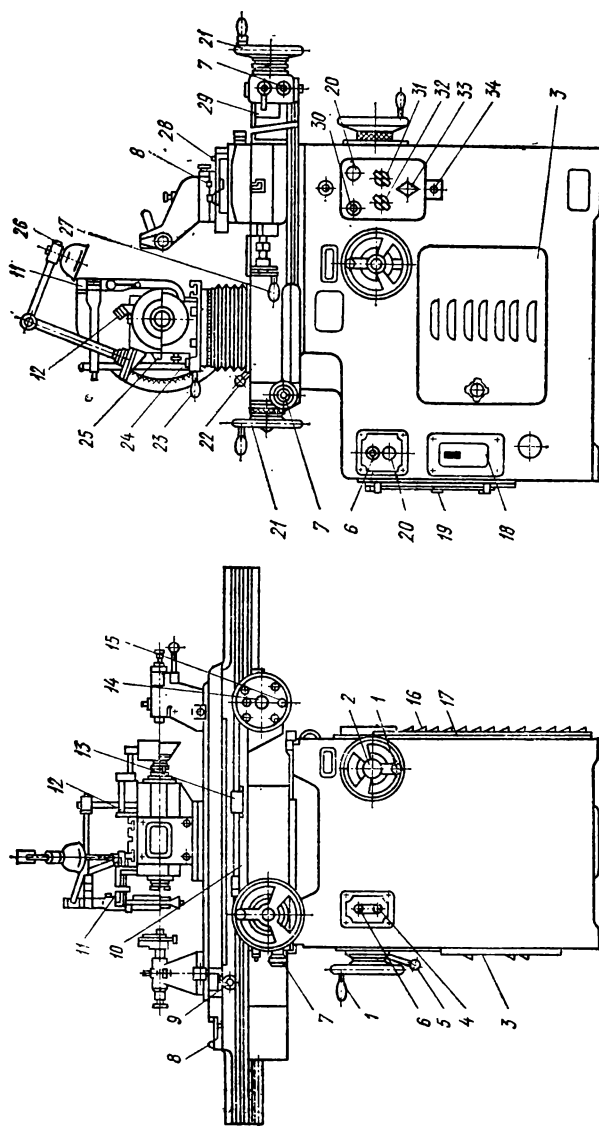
Расположение органов управления универсально-заточного станка мод. 3B642:
